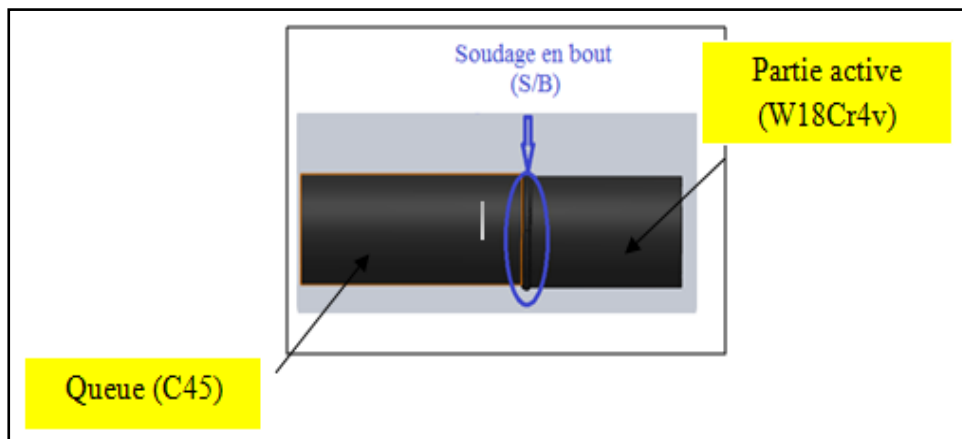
Soudage en bout de deux morceaux.
